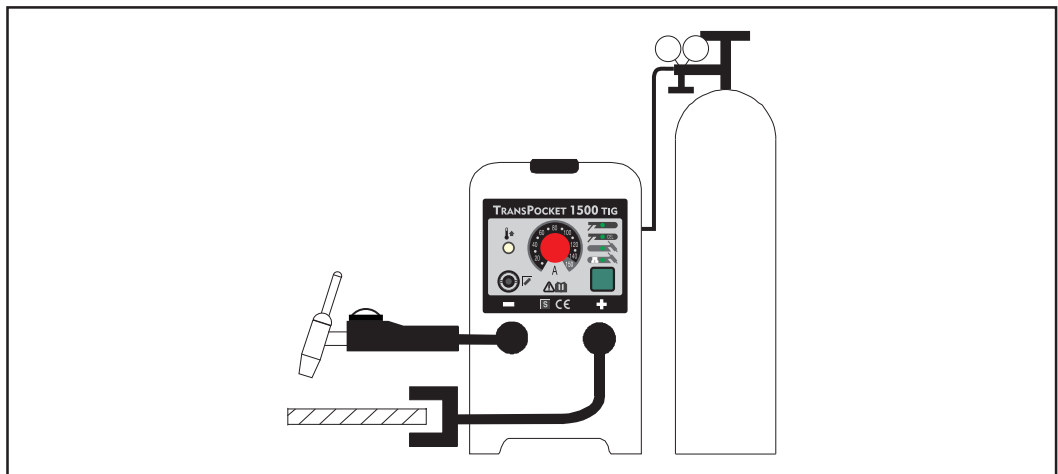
TP 1500 TIG ausgerüstet mit Schweißbrenner AL 1500
